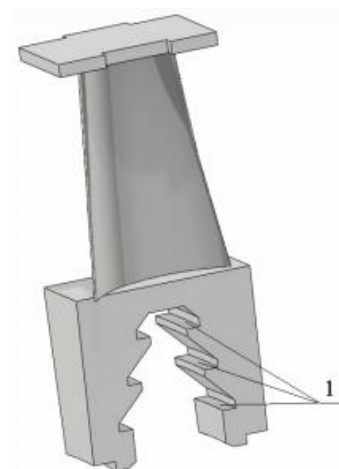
Робоча лопатка з опорними поверхнями (поз. 1)
